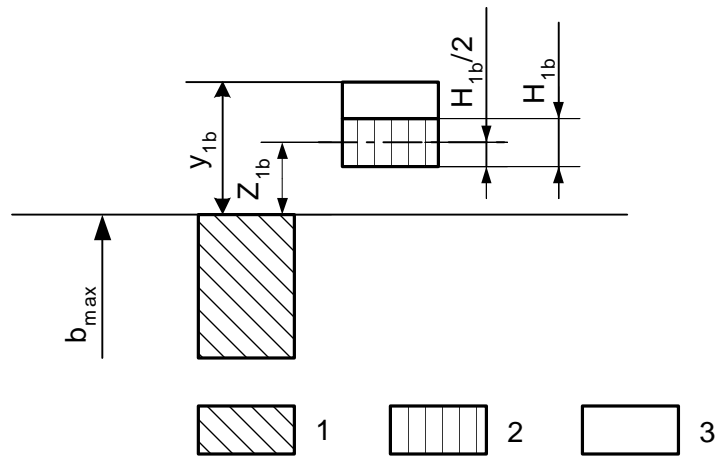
Схема расположения полей допусков диаметров  $d_k$  и  $D_k$  калибров-колец (1 – поле допуска центрирующего диаметра  $d$  или  $D$  вала; 2 - поле допуска на изготовление калибра-кольца; 3 - поле износа калибра-кольца)
